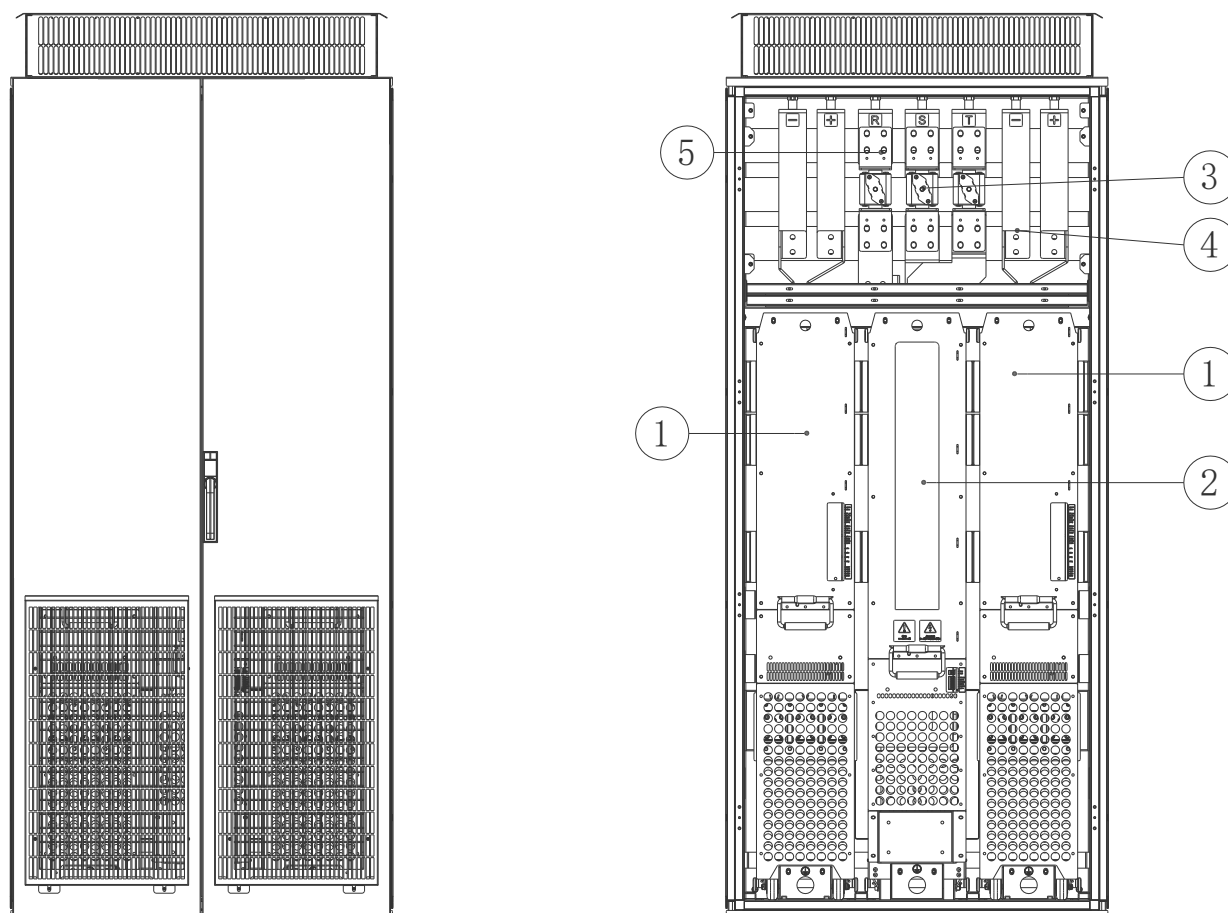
Компоновка шкафа активного выпрямителя корпуса LCL+2FR8
